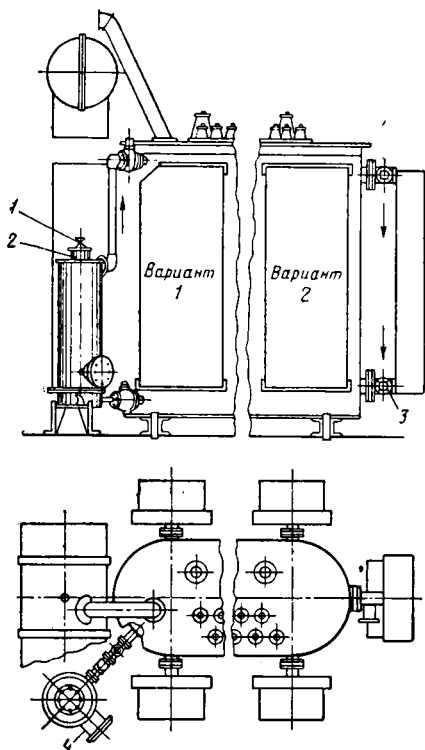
Установка фильтра на трансформаторе с волнистыми стенками бака и без радиаторов
